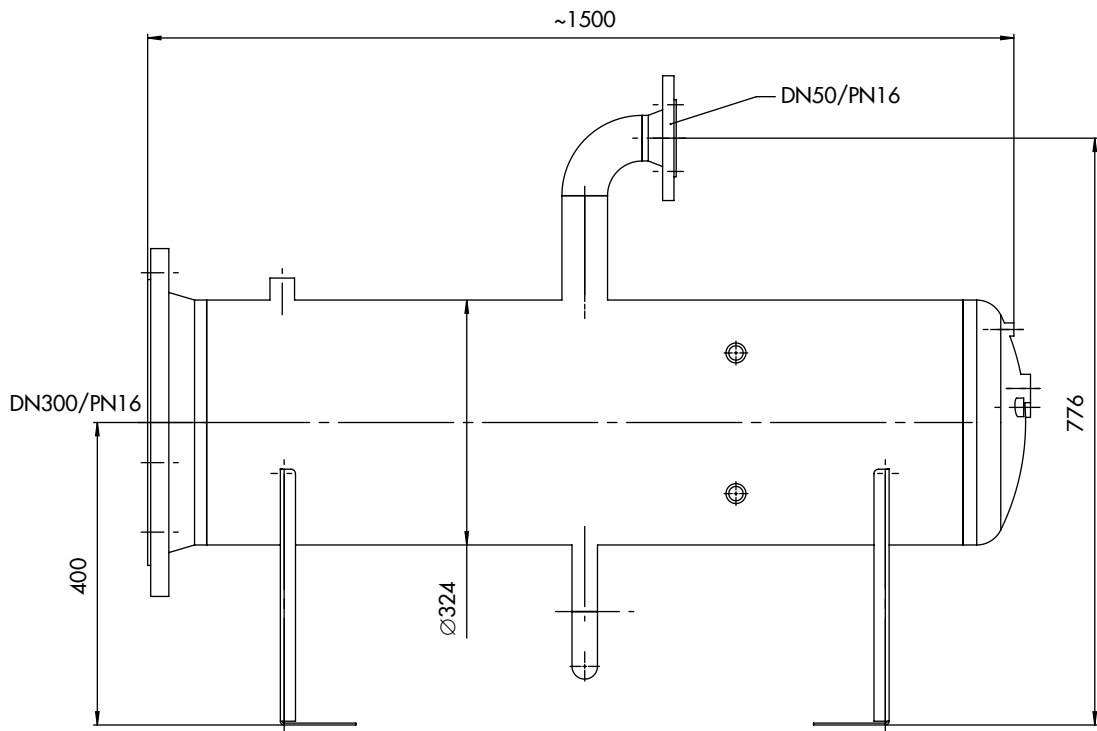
Elektrischer Dampferzeuger Typ 7120 · Abmessungen
